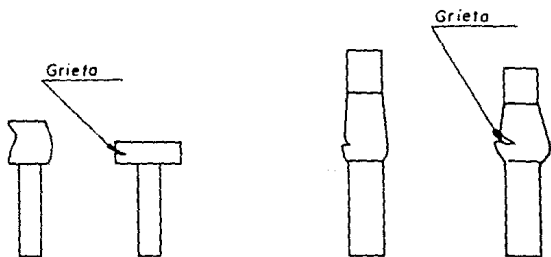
Este tipo de defectos es muy común al hacer la cabeza de un tornillo.
